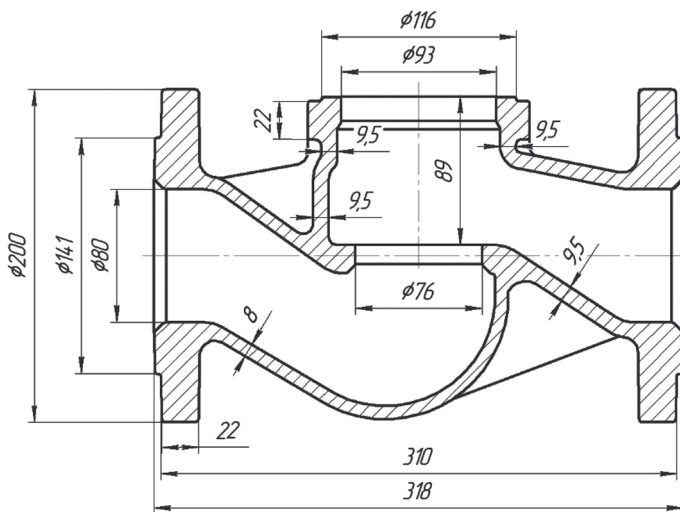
Чертеж отливки «Корпус вентиля ДУ80»
